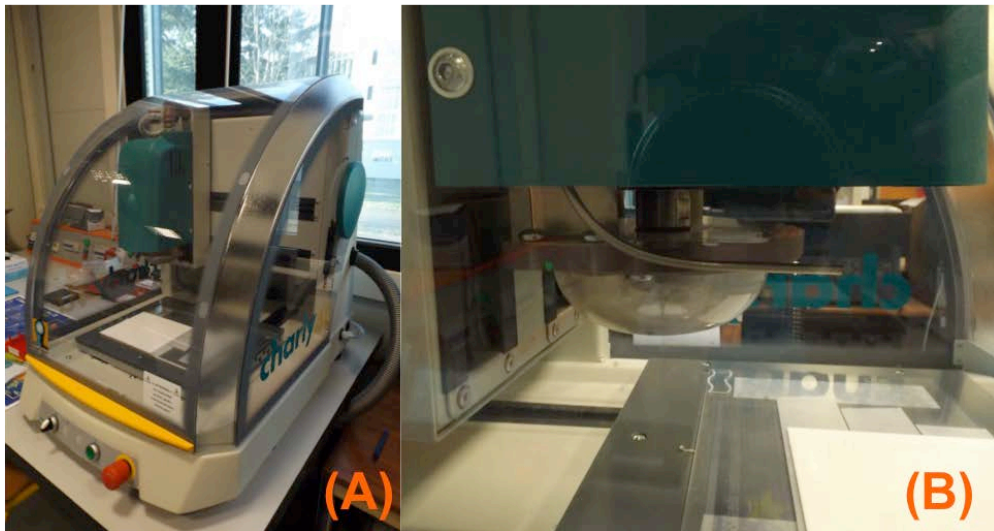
Machine de fraisage 2D Charly 4U avec le setup de manipulation
